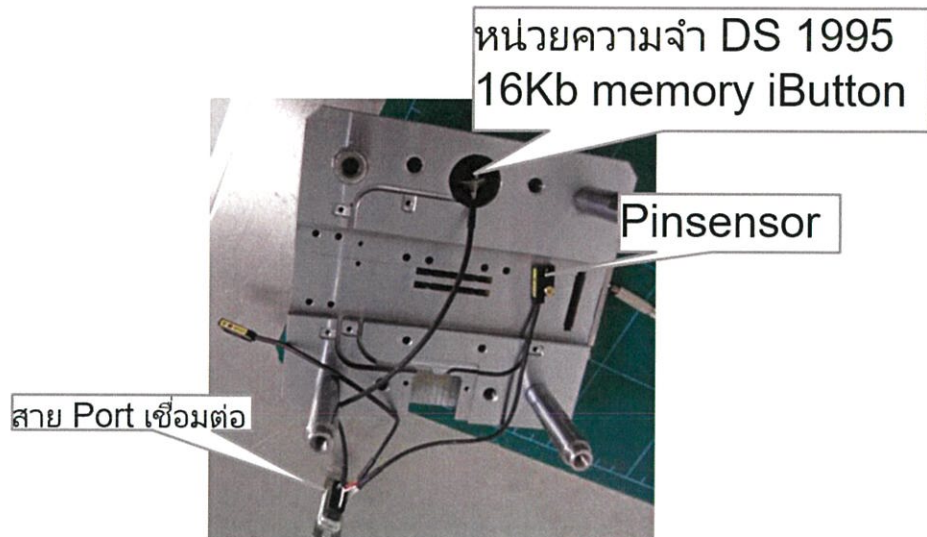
เครื่องมือ Cutting Tool ที่ทำการ Modify เสร็จเรียบร้อยแล้ว
